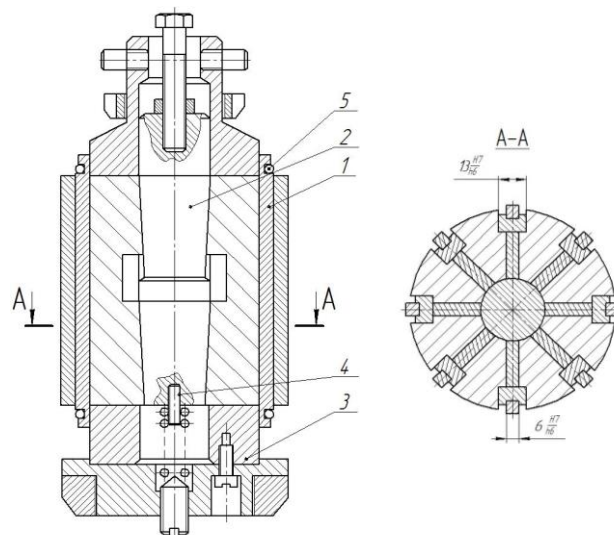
Опытная хонинговальная головка: 1 – колодка; 2 – шток; 3 – корпус; 4 – упор; 5 – пружина
